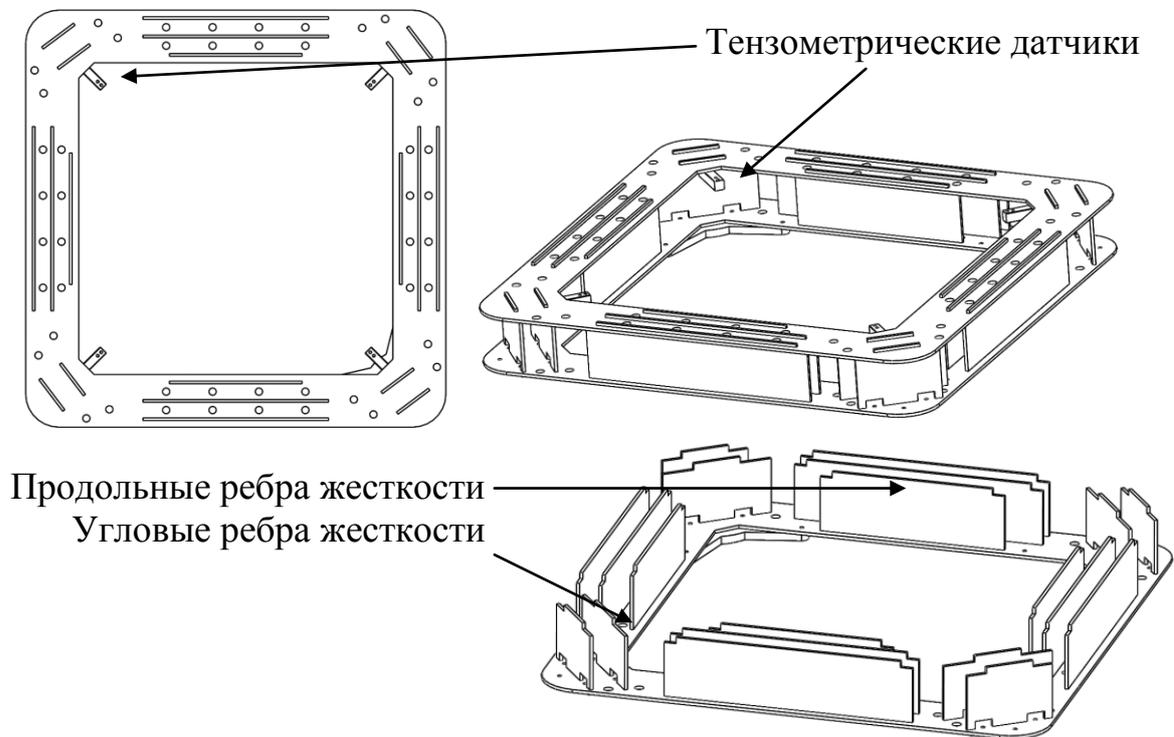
Конструкция новой модели станда. Базовый четырехгранник, вертикальный и поступательный шарниры скрыты
